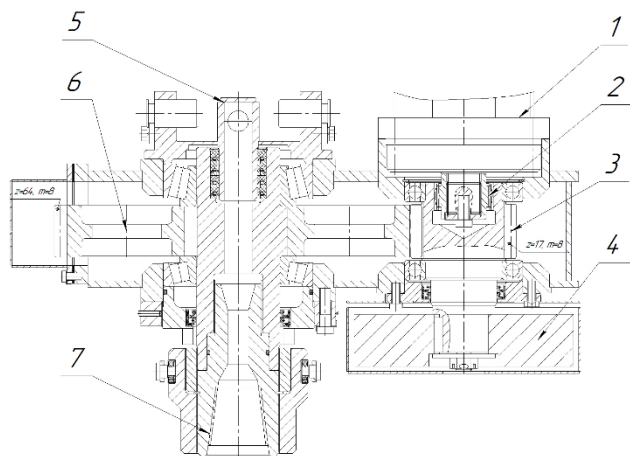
Одноступенчатый редуктор, применяемый в конструкции с использованием низкомоментного гидромотора и редуктора:
